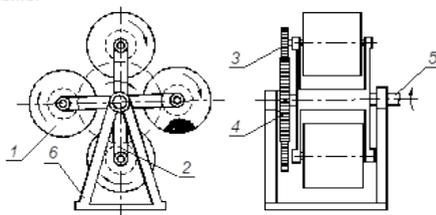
Планетарная мельница: 1 – барабанная мельница; 2 – водило; 3 – приводная шестерня; 4 – неподвижное зубчатое колесо; 5 – приводной вал; 6 – станина
